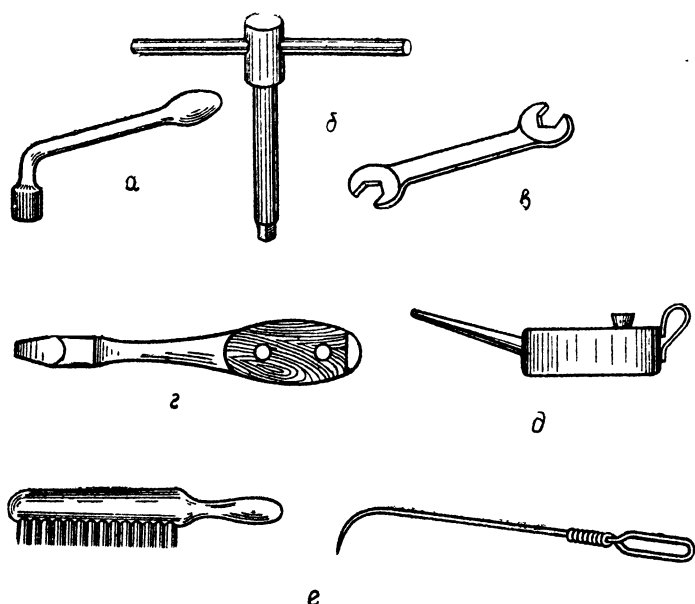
Вспомогательный инструмент и принадлежности токарно-винторезного станка:
